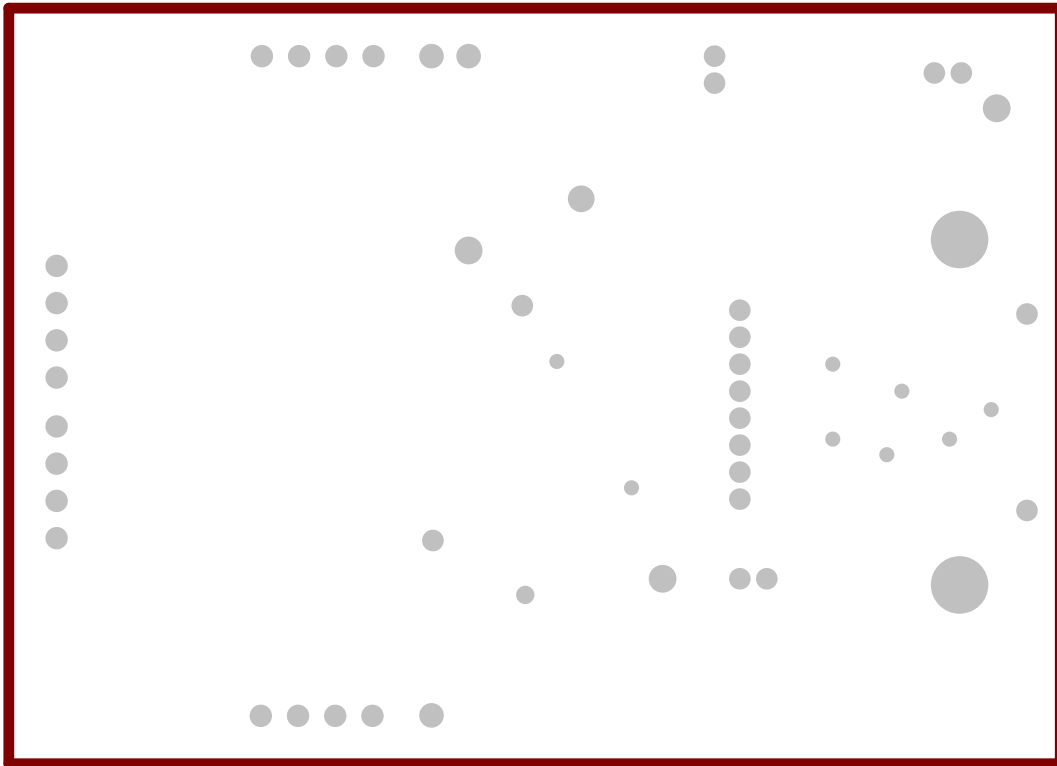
ADS125P08 評価基板 PCB レイアウト — グランド層 2
